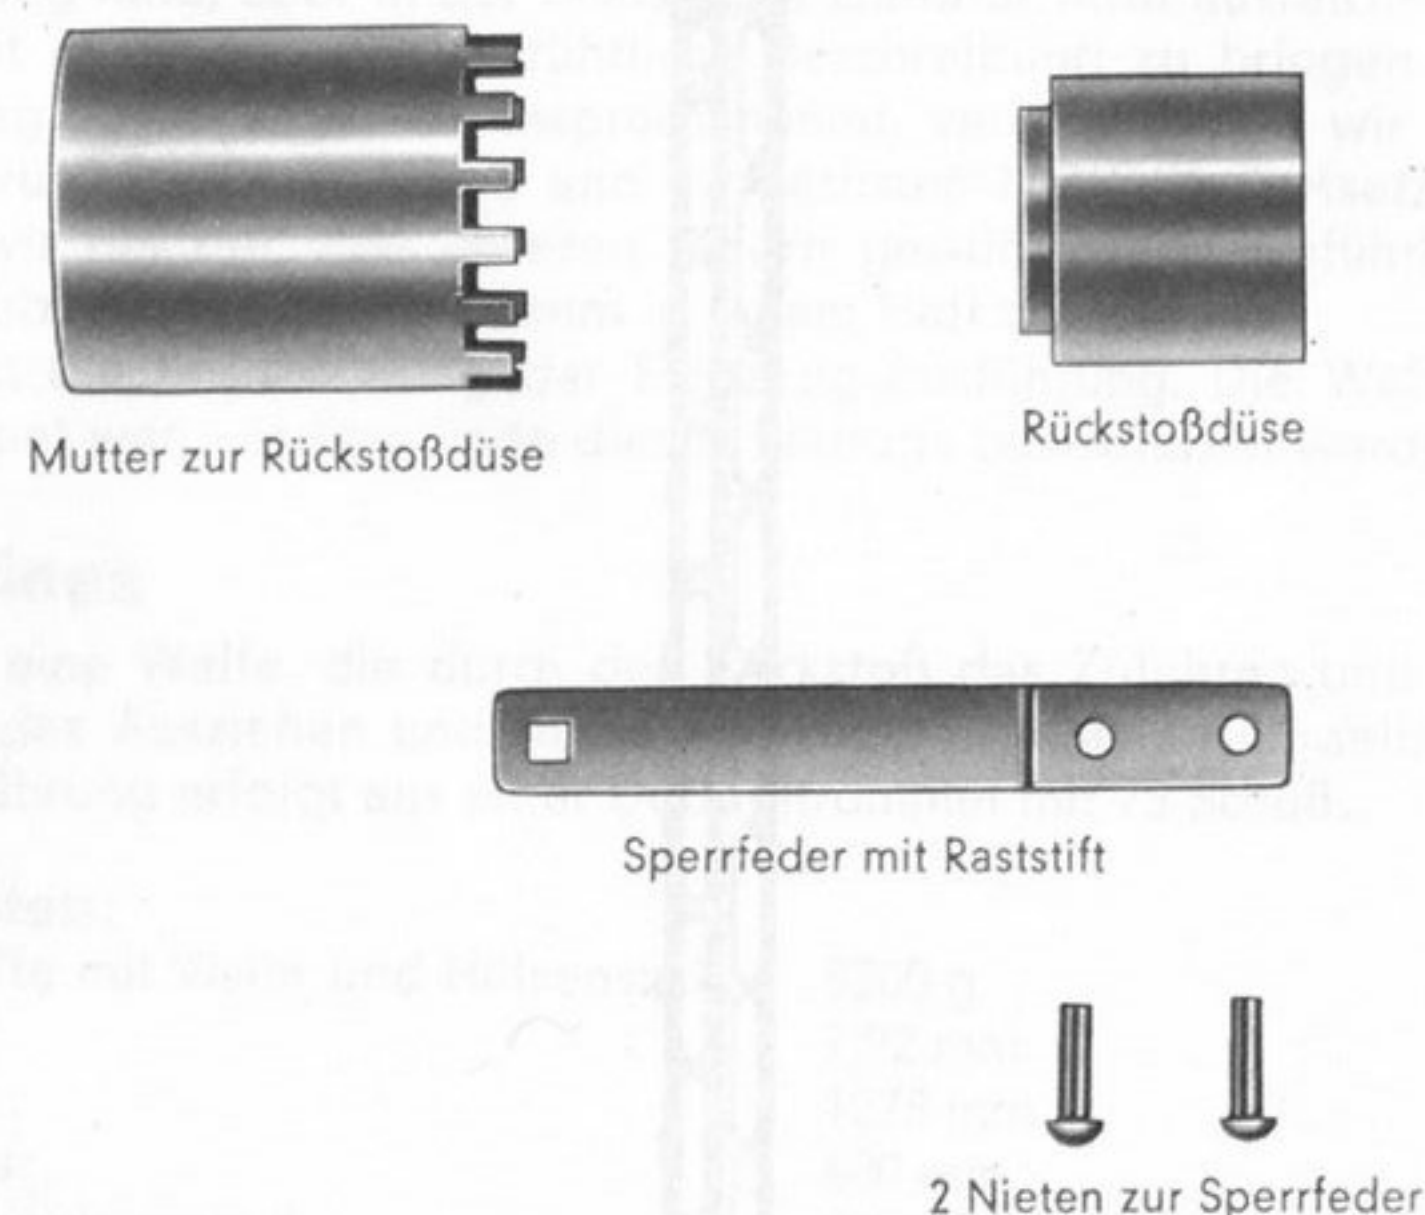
Rückstoßdüse und Teile zur Befestigung der Rückstoßdüse
